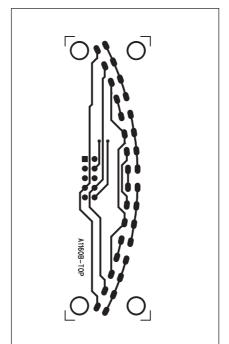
Obrazec desky spojů řídicí jednotky (strana TOP)
